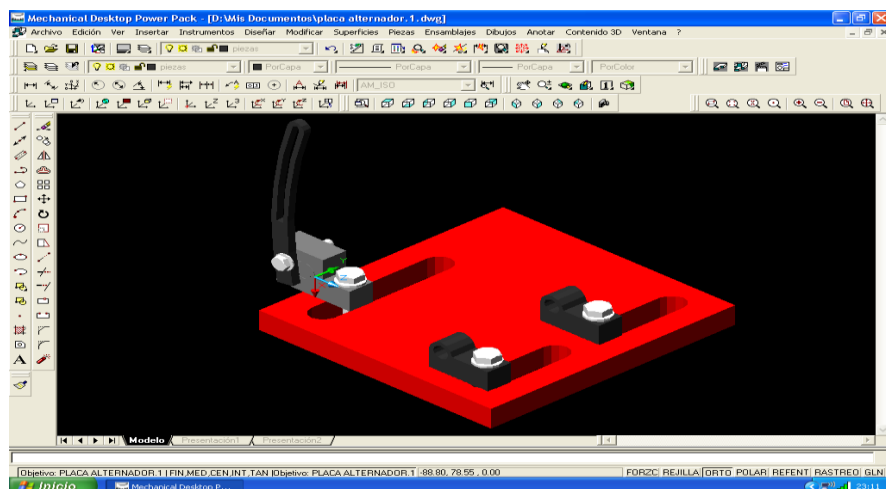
Vista isométrica 1 de la placa que soporta el alternador
